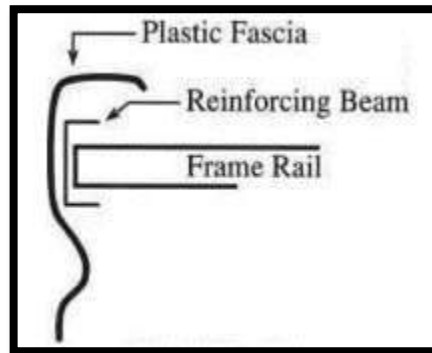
Mascarilla de plástico y viga de refuerzo.
